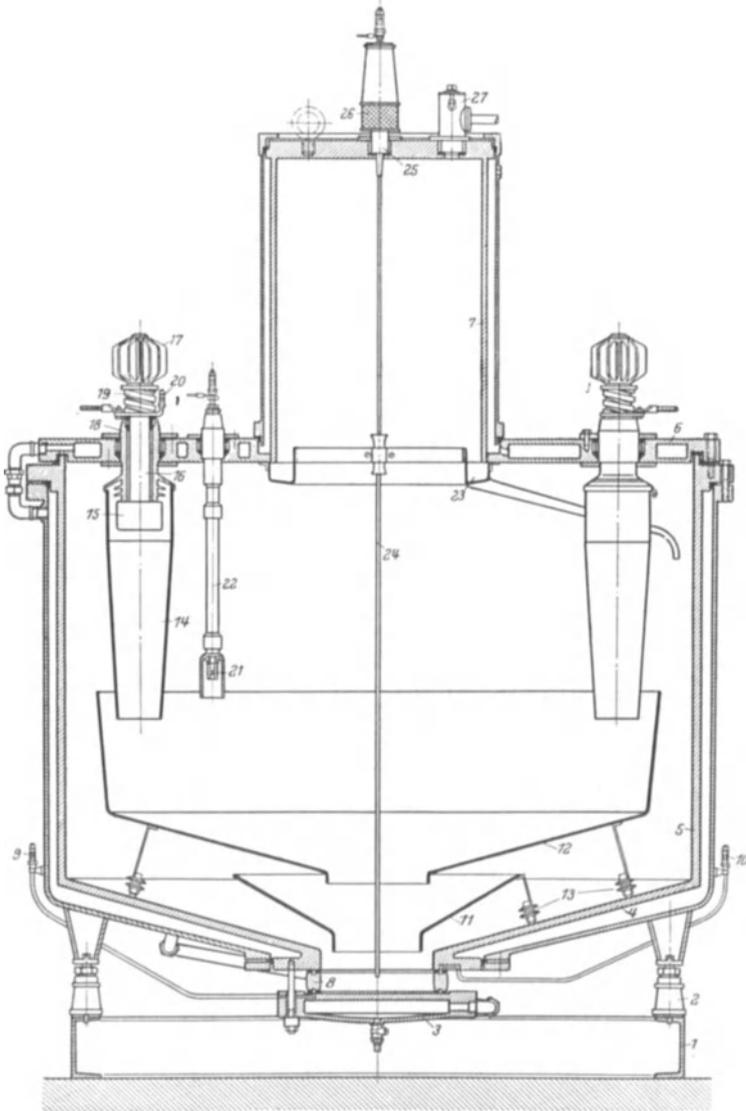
Schnitt durch einen B.B.C.-Eisen-Großgleichrichter.
